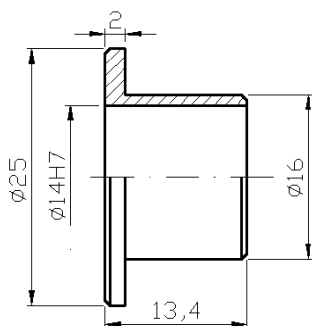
Geometria e dimensões do inserto metálico (dimensões em mm).
